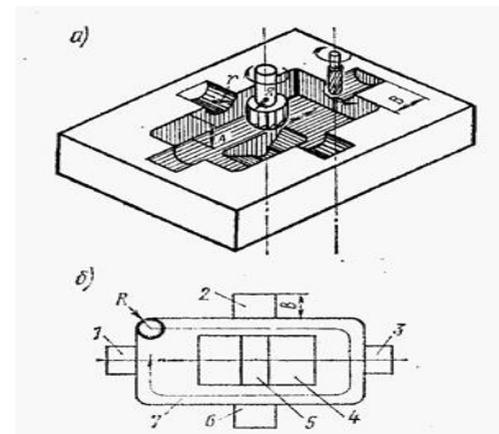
Пример обработки поверхностей штампа радиусным фрезерованием методом настройки
